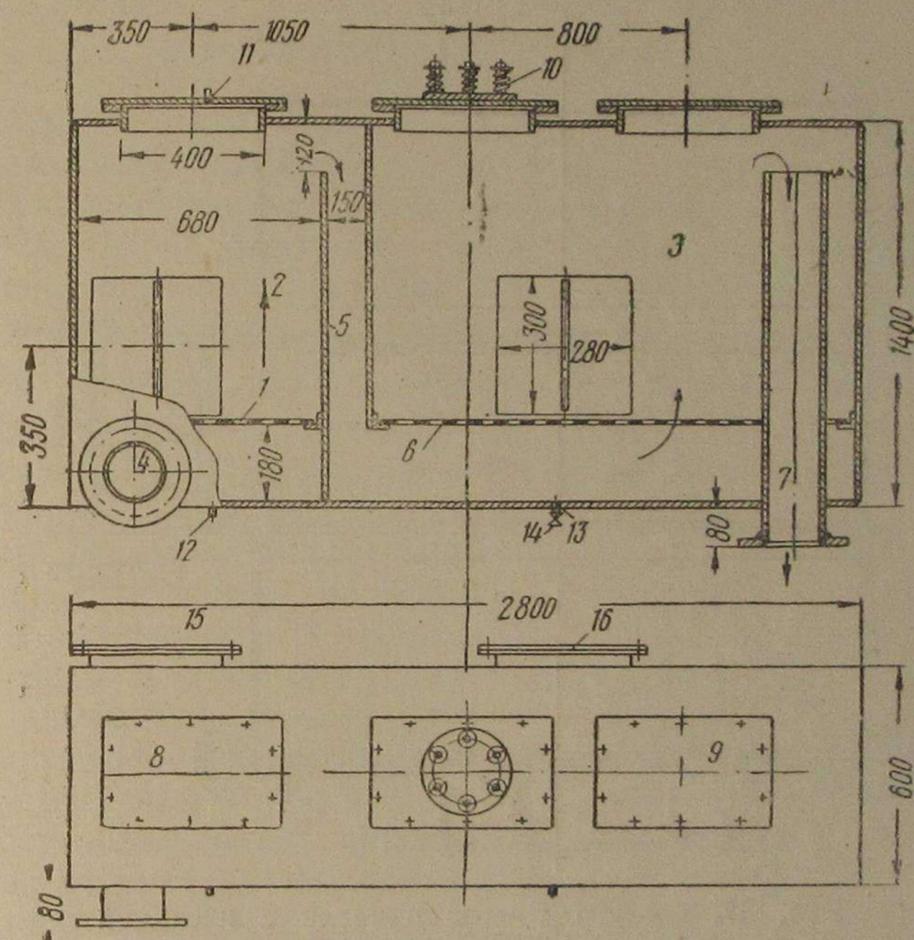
Фильтр тонкой очистки с коксовой и древесной насадками
